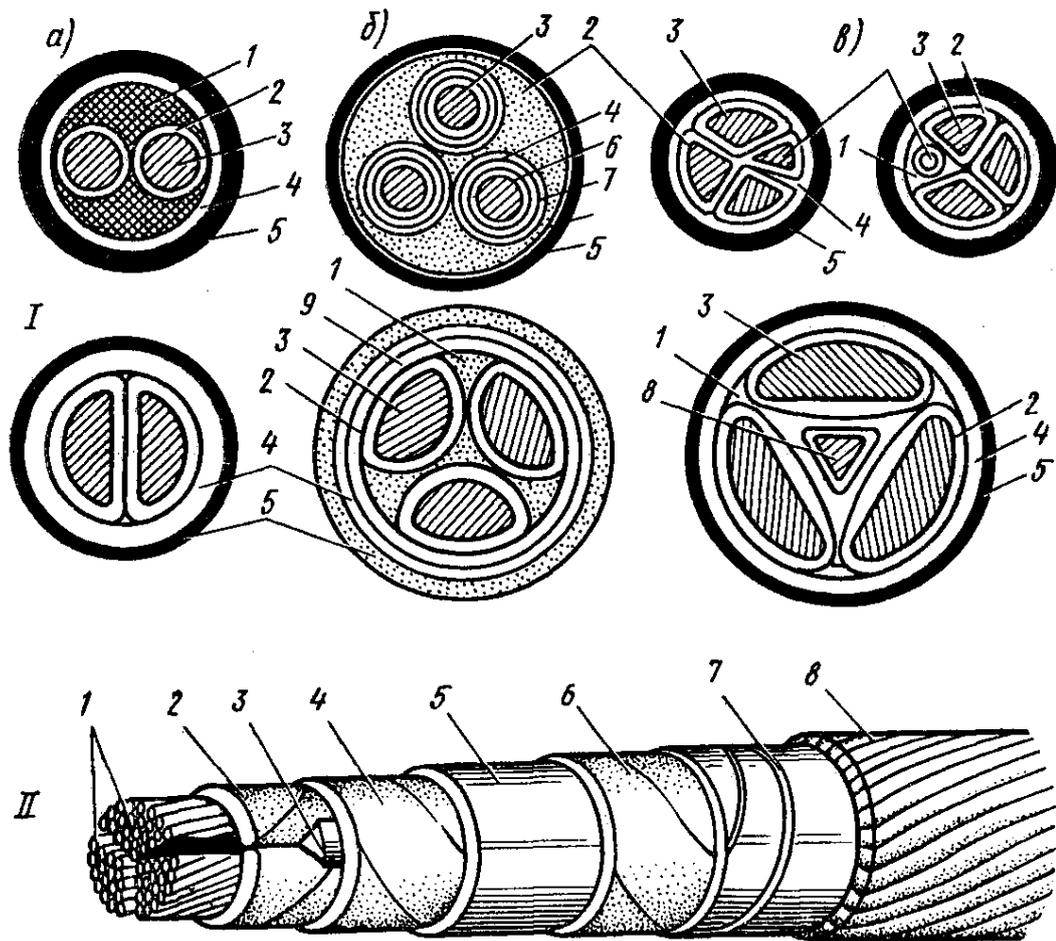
Конструкция силового кабеля: 1 - сечение силовых кабелей: а - двухжильные кабели с круглыми и сегментными жилами; б - трехжильные кабели с поясной изоляцией и отдельными оболочками; в - четырех жильные кабели с нулевой жилой, круглой, секторной и треугольной формы; 1 - заполнитель; 2 - изоляция жилы; 3 - токопроводящая жила; 4 - оболочка; 5 - наружный защитный покров; 6 - экран на токопроводящей жиле; 7 - бронепокров; 8 - нулевая жила; 9 - поясная изоляция; II - силовой трехжильный кабель марки ААБ: 1 - токопроводящие жилы; 2, 4 - фазовая и поясная изоляция; 3 - наполнители; 5 - оболочка; 6 - защитный покров оболочки (подушка); 7 - броня из стальных лент; 8 - наружный защитный покров
